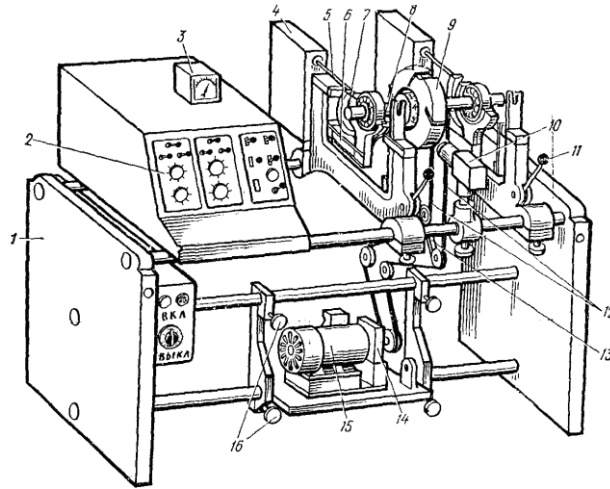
Верстат для динамічного балансування ДБ-10: 1 — станина, 2 — електровимірювальний пульт, 3 — прилад для виміру величини дисбалансу, 4 — вимірювальний перетворювач, 5 — стрижень, 6 — коліска, 7 — опора, 8 — оправлення, 9 — балансуємий інструмент, 10 — стробоскопічна головка, 11 — рукоятка гальма коліска, 12 — ремінь, 13 — ленікс, 14 — гальмо електродвигуна, 15 — електродвигун, 16 — рукоятка затискача каретки
